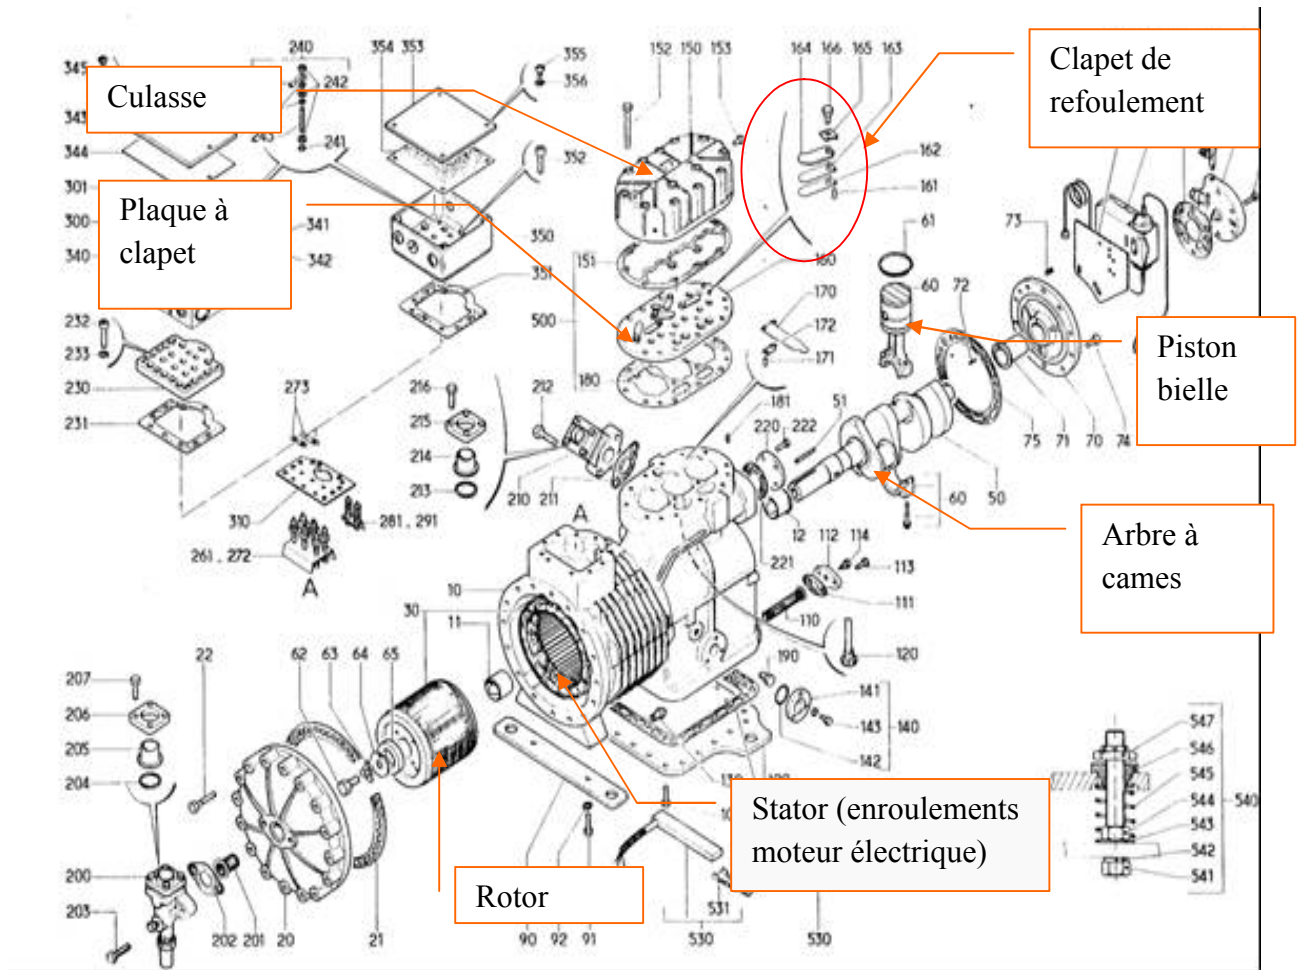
Vue éclatée d'un compresseur à piston [17]
